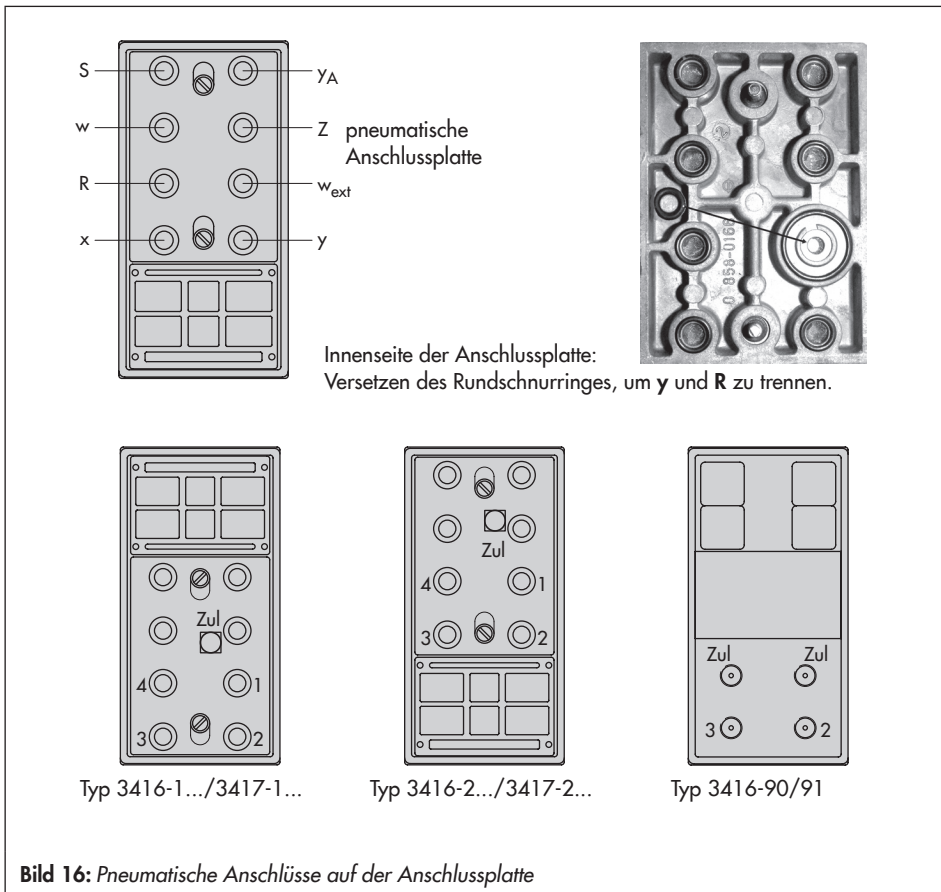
Pneumatische Anschlüsse auf der Anschlussplatte
